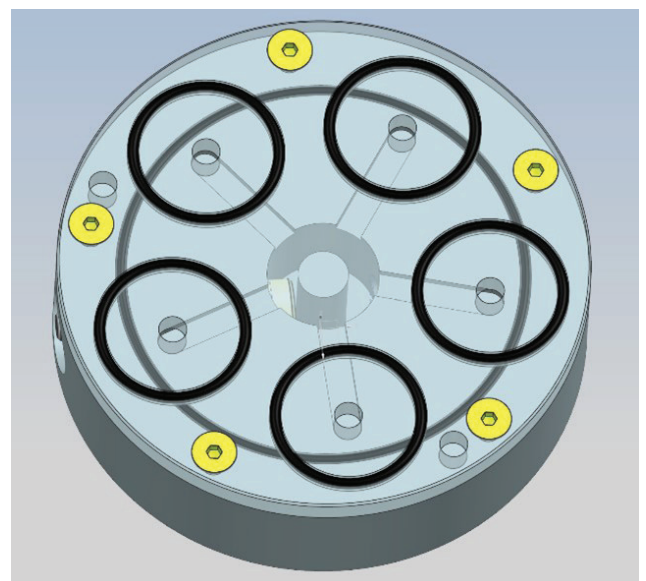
Prototyp 2 der Spannvorrichtung mit transparenter Spannplatte, um die Luftkanäle und das Innere der Vorrichtung ersichtlich zu machen
